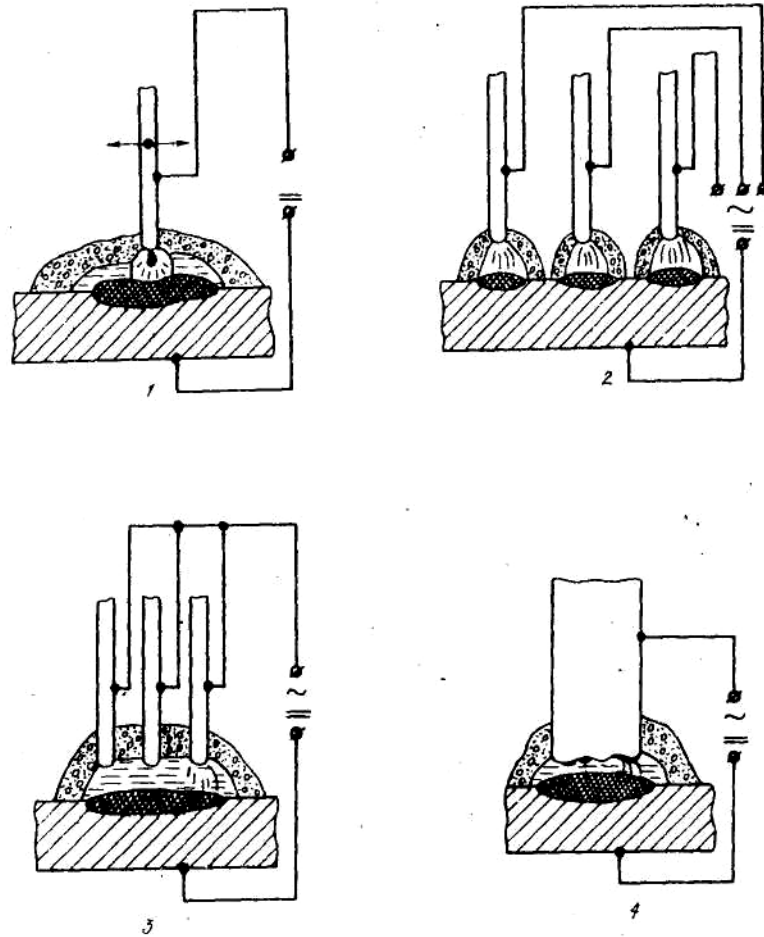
Варіанти наплавлення шийок валів центрифуг під шаром флюсу (зліва направо):
